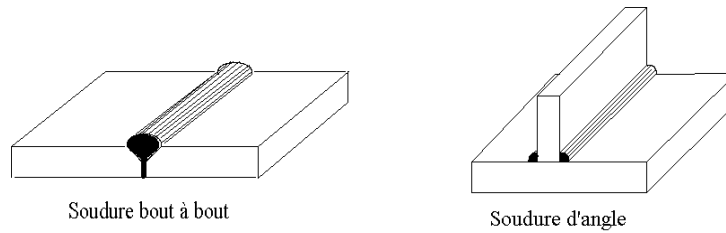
Exemple d'assemblage de deux pièces par soudure
